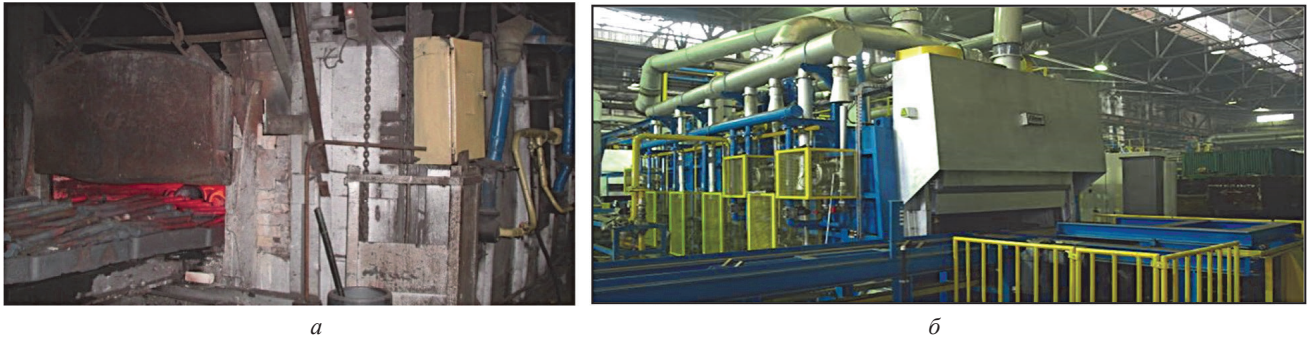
Оборудование термического участка кузнечного цеха: *а* – толкательный агрегат старой конструкции; *б* – толкательный агрегат нормализации APN-1800G
